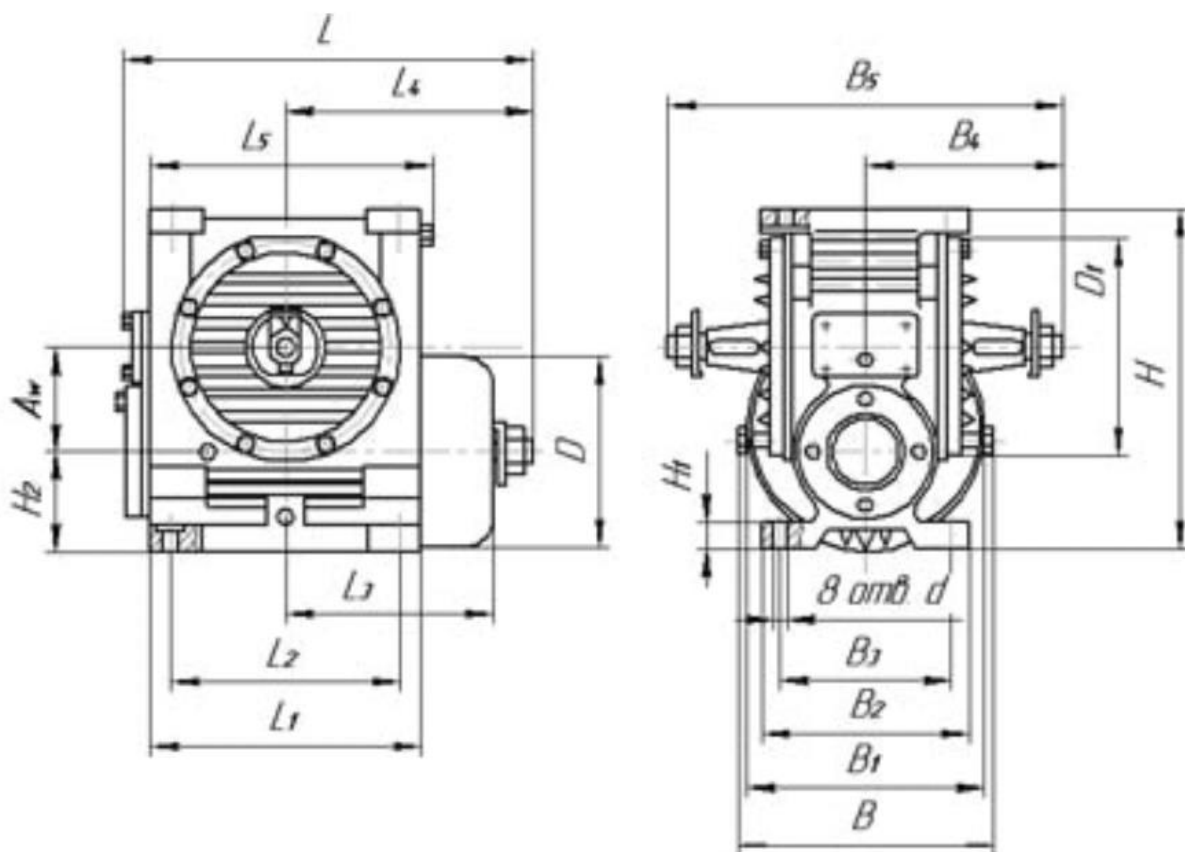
Габаритные и присоединительные размеры Ч-100
